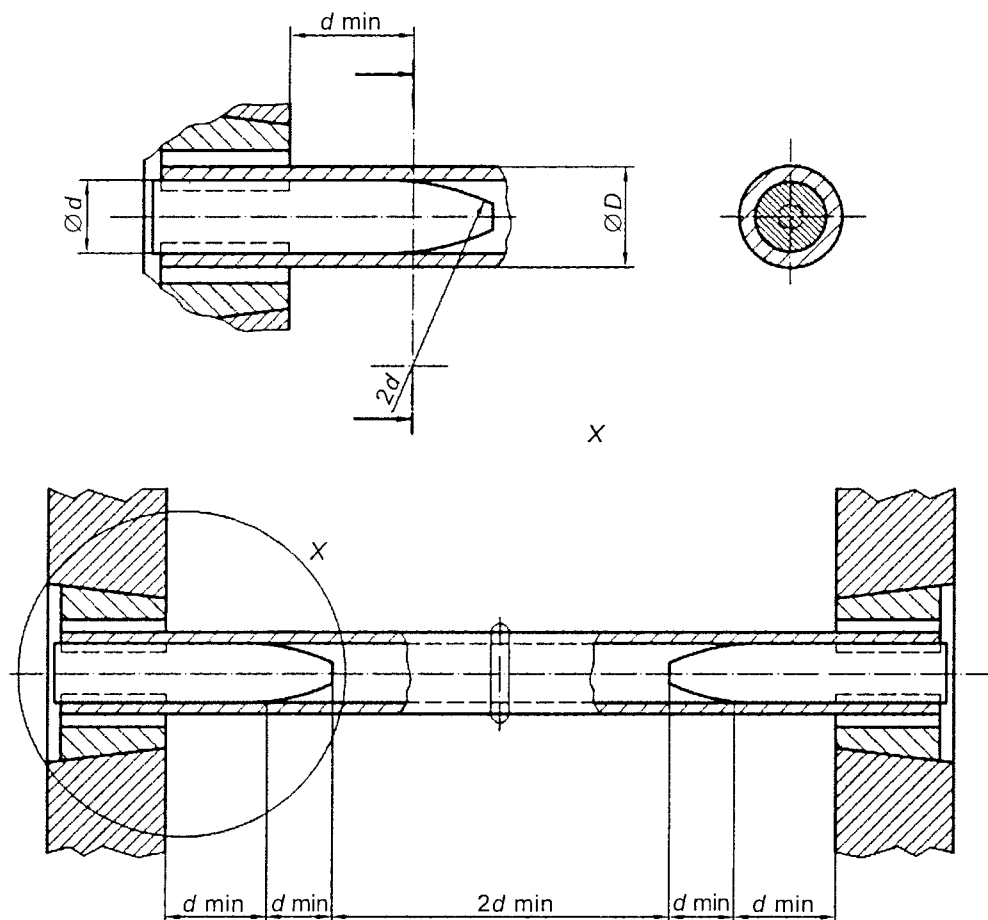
Випробний зразок на розтягування труби повного перерізу
